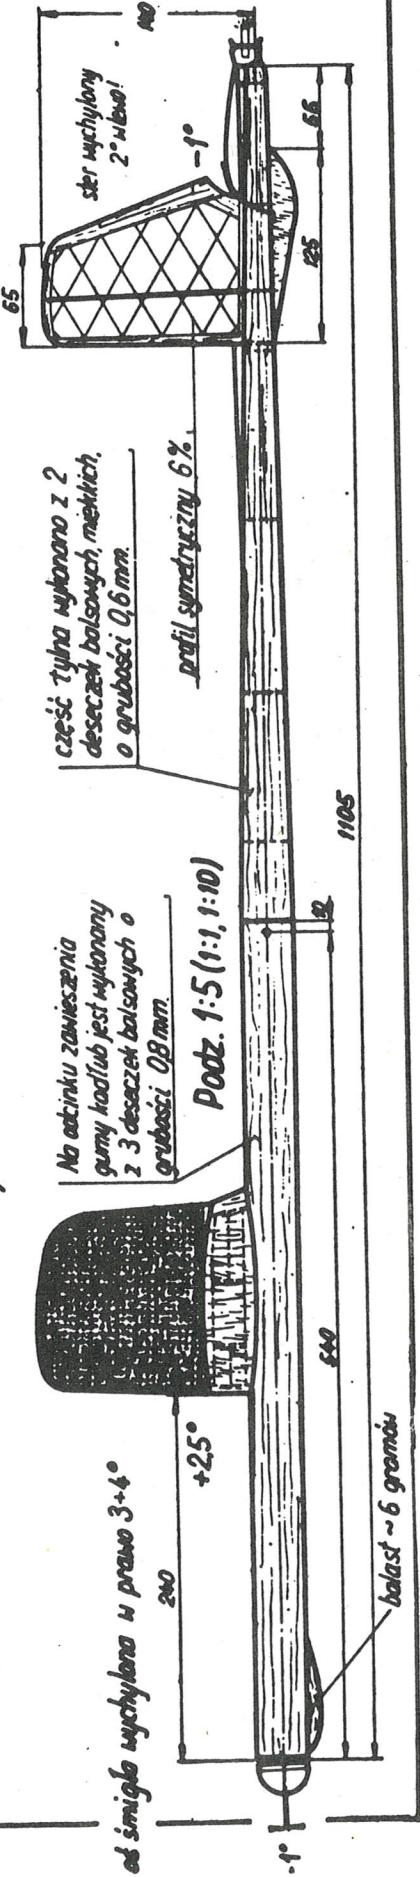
FIGURE DE CONSTRUCTION POLONAISE : NÉTTO J.
